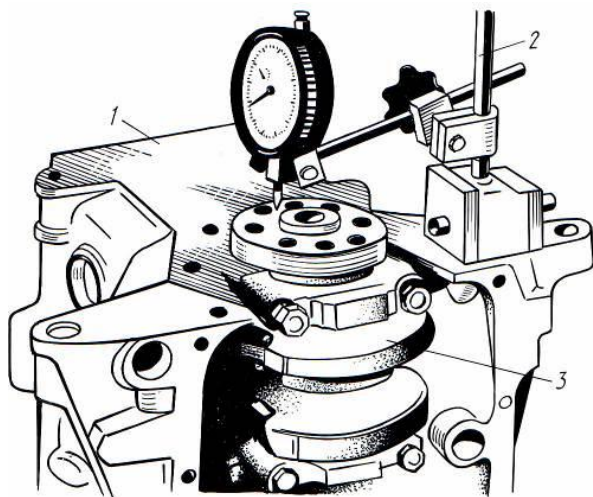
Проверка осевого люфта коленчатого вала индикатором часового типа:
